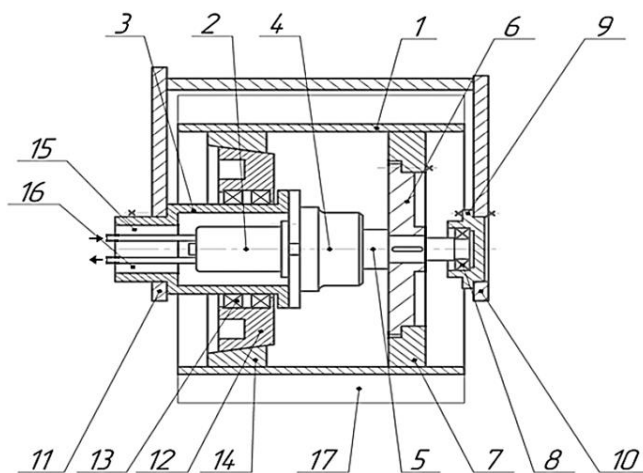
Конструктивна схема фрезерного барабана МХФ
